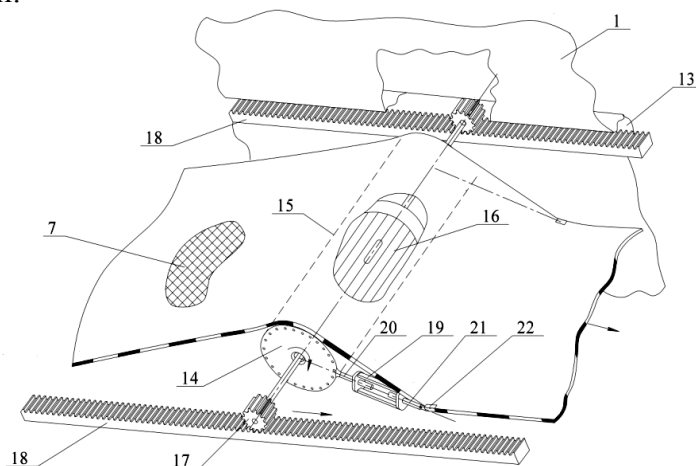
Ворошитель: 1 – корпус; 7 – лента; 13 – паз; 14 – крышка; 15 – барабан; 16 – электродвигатель; 17 – зубчатое колесо; 18 – зубчатая рейка; 19 – трубуцина; 20, 21 – шпильки; 22 – направляющие
